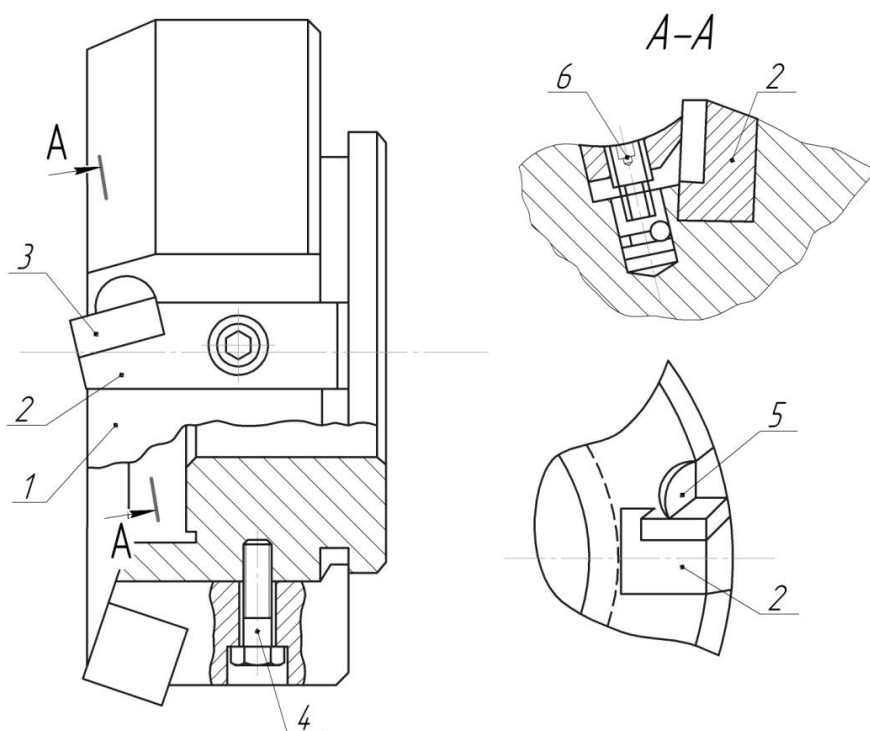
Фреза торцовая с клиновым креплением пластин
